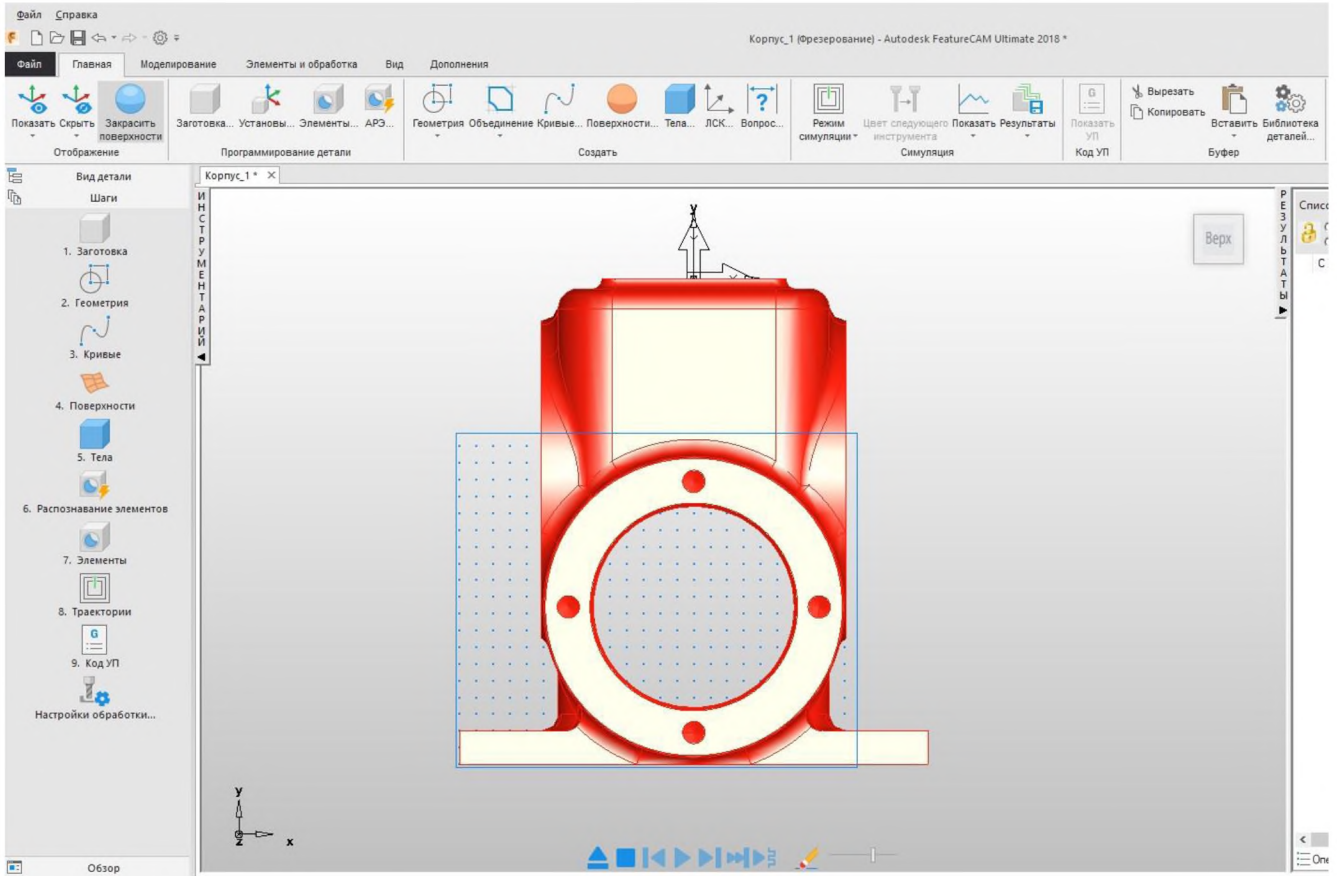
Корпус редуктора ЦВ-40 у Autodesk FeatureCAM
